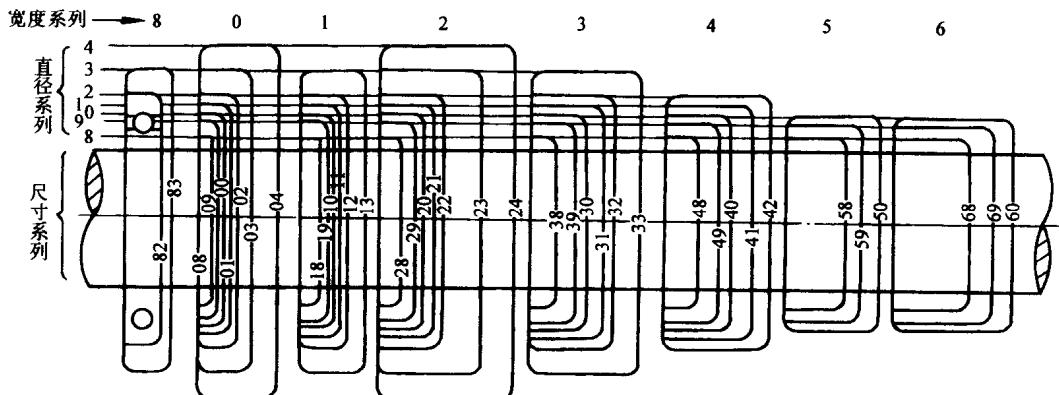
向心轴承的尺寸系列示意图（圆锥滚子轴承除外）
